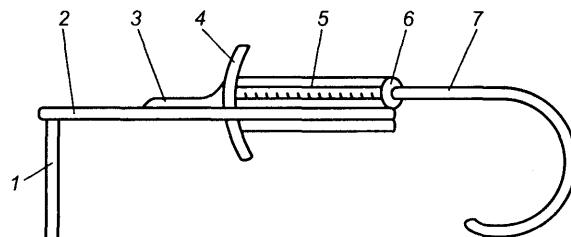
Электрододержатель для сварки с предварительным нагревом:
